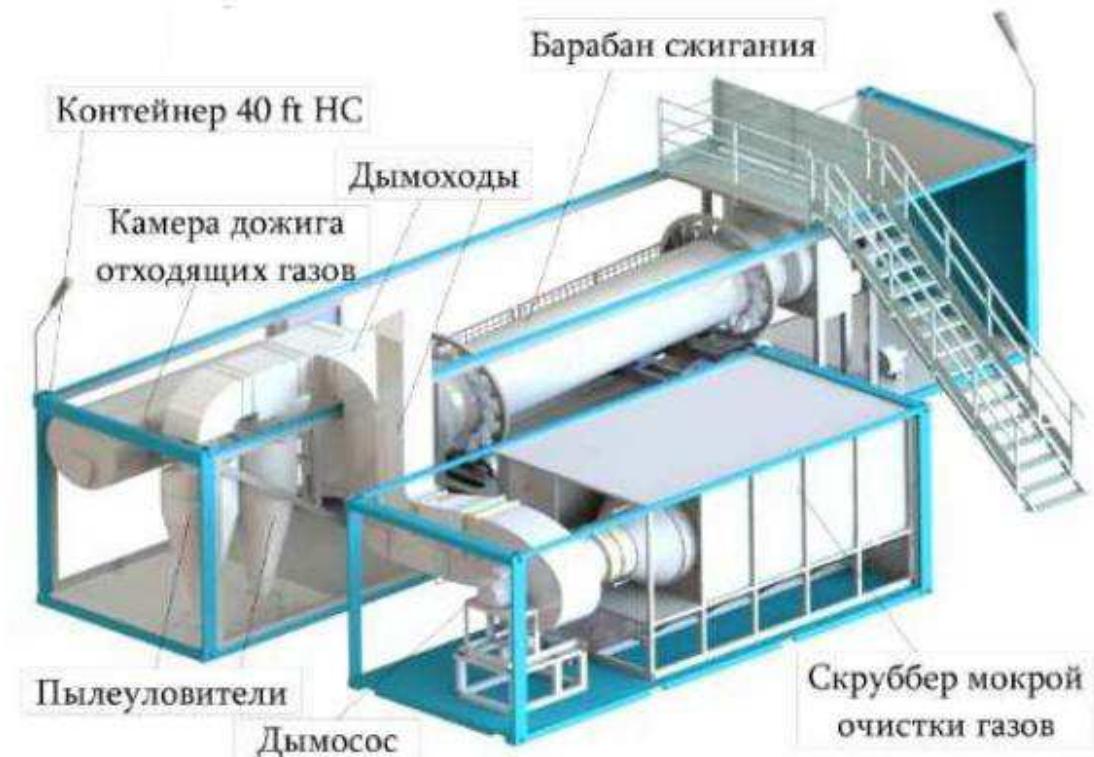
Общий вид «ТДУ Фактор – 500» (вид слева) [20]
